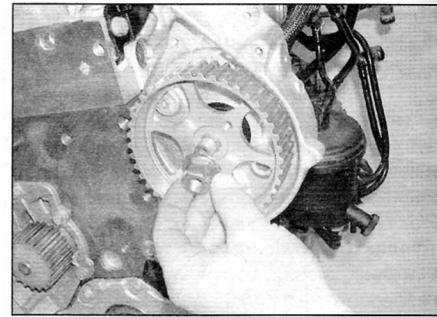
, в. После высвобождения зубчатого шкива снимите съемник, а затем отверните гайку и снимите зубчатый шкив (двигатели 2.0 л)
